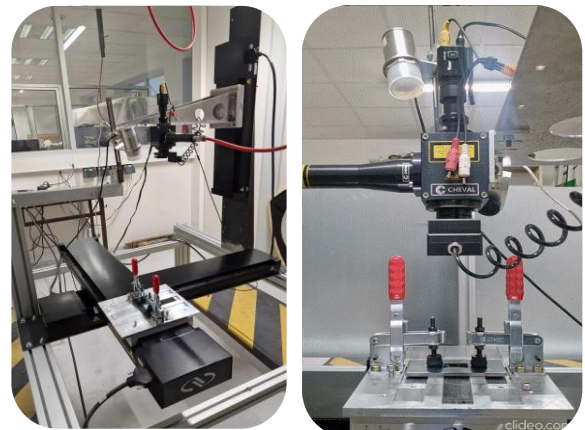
(a) Configuration du procédé de soudage laser Nd:YAG, (b) Système de Clampage pour l'étape d'assemblage
